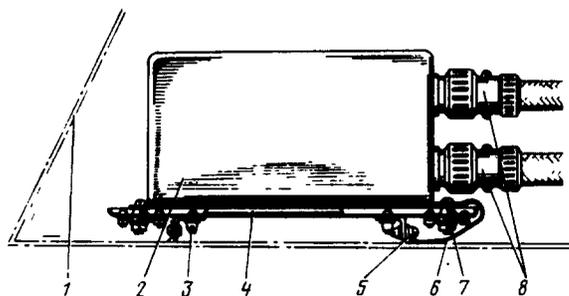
Установленный исполнительный блок ССП-ФК-БИ:
